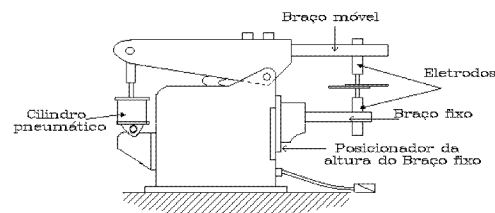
Ilustração de uma Máquina para Soldagem por Resistência Elétrica.
